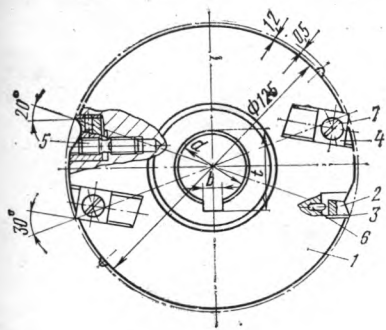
Фреза, оснащенная поворотными режущими пластинами с четырьмя рабочими кромками
